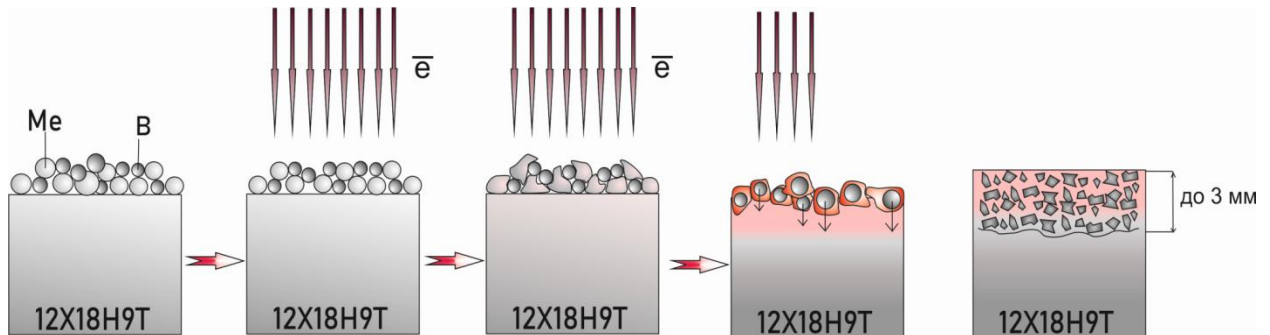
Схема процесса наплавки порошковой смеси в присутствии смачивающего компонента
